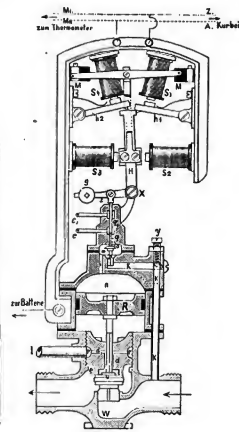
Selbstthätiger Universal-Regler von F. Butzke & Co., Berlin.
